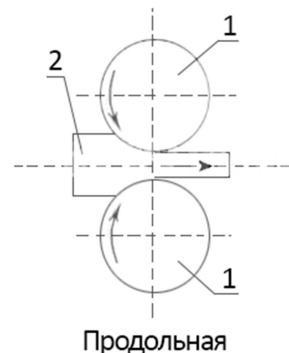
Схема продольной прокатки: 1 – валковая пара; 2 – тело заготовки.
